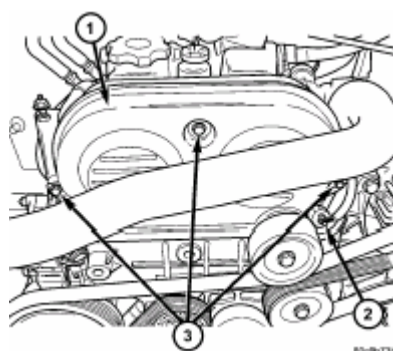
Верхняя крышка ремня газораспределительного механизма/болты:
